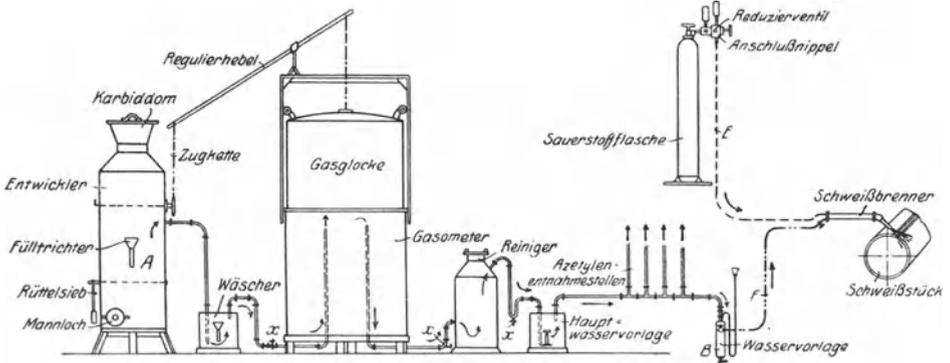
Schema einer ortsfesten Azetylschweißanlage.
